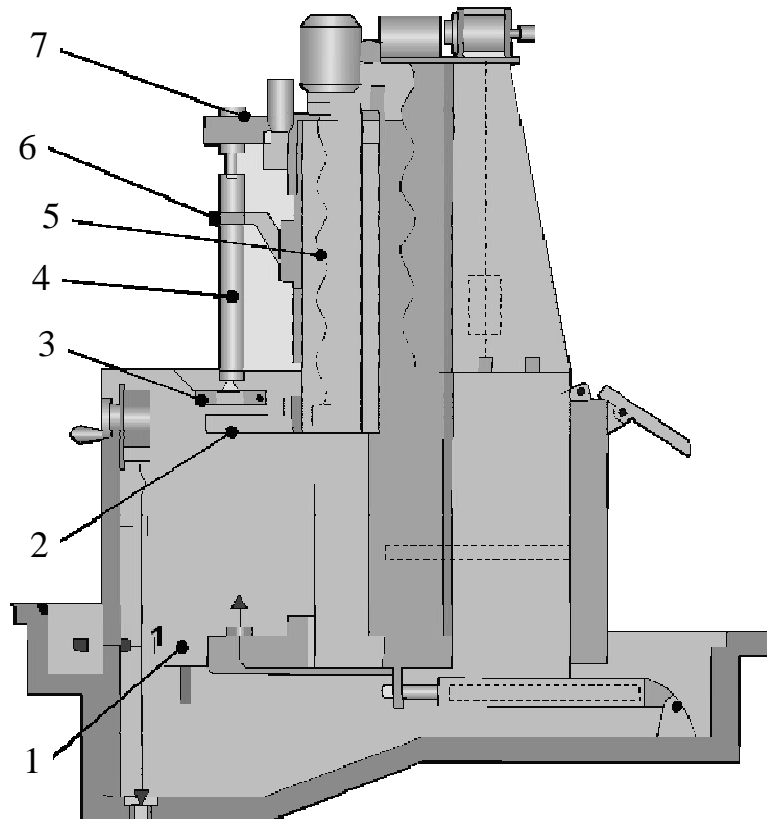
Схема універсального агрегатного верстата для гартування деталей типу тіл обертання
